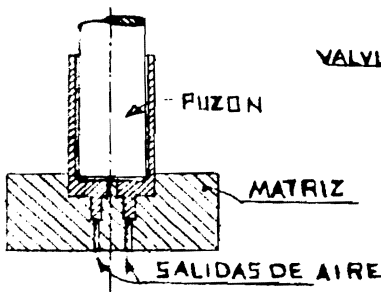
Util para extruir - el cartucho fumígeno de - la Fig. 10,
